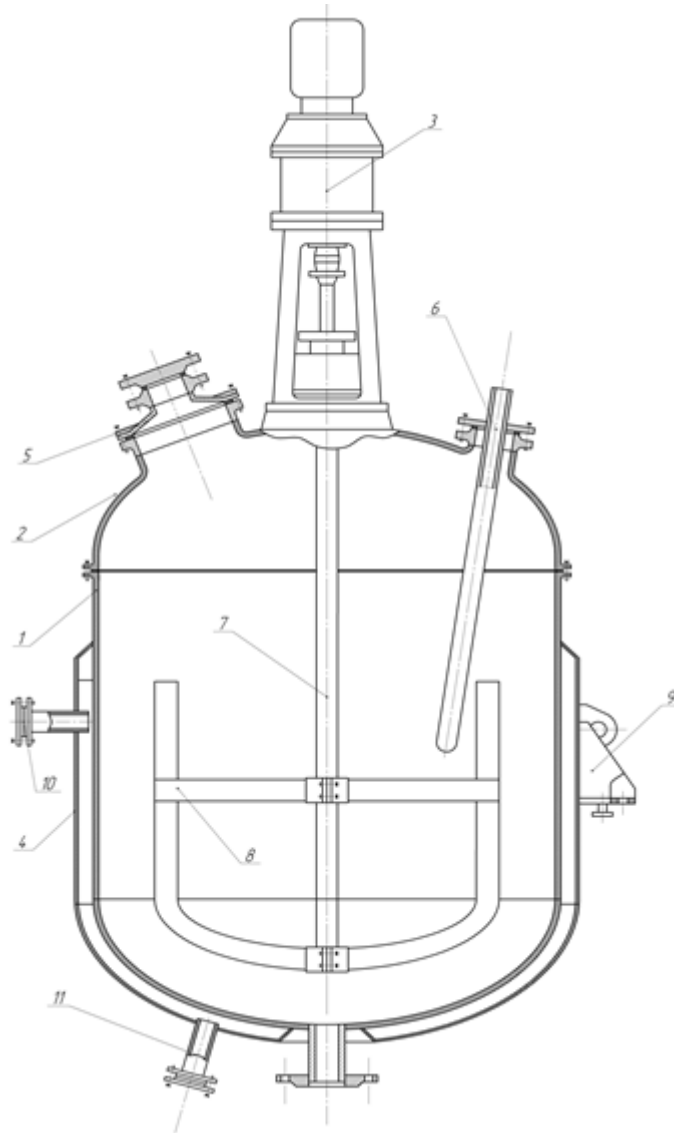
Апарат для змішування розчинів: 1 – корпус; 2 – кришка; 3 - привод з електродвигуном; 4 - сорочка; 5 - люк; 6 – гільза термометра; 7 - вал мішалки; 8 - мішалка; 9 - опора; 10 - штуцер для входу теплоносія; 11 - штуцер для виходу теплоносія; 12 - штуцер для злива розчину.
